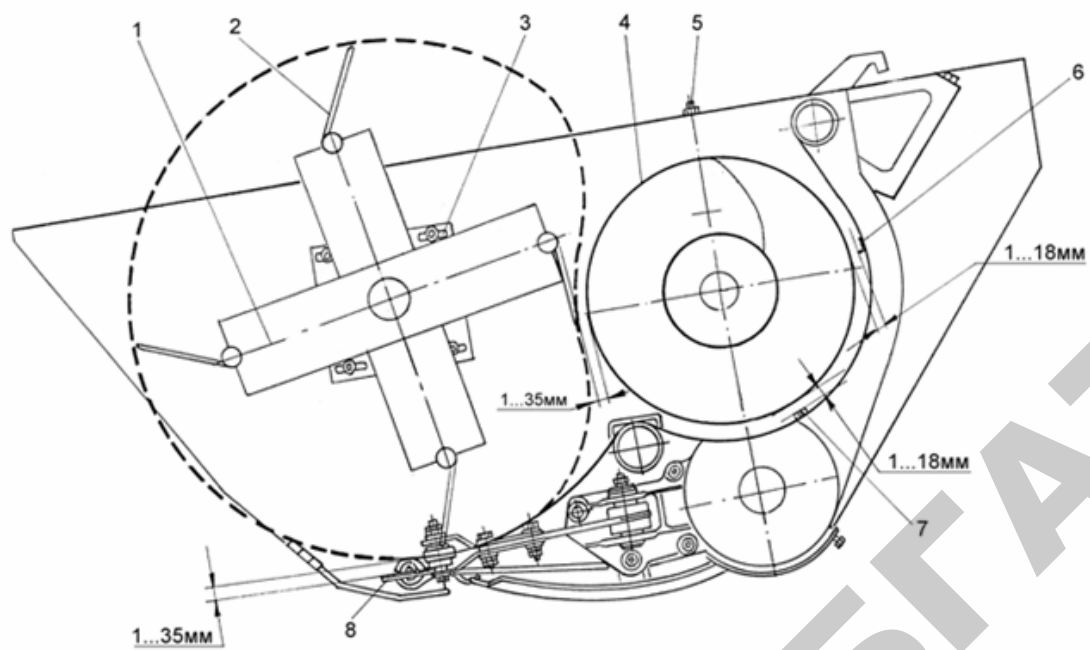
Регулировка положения мотовила и шнека жатки для трав:
